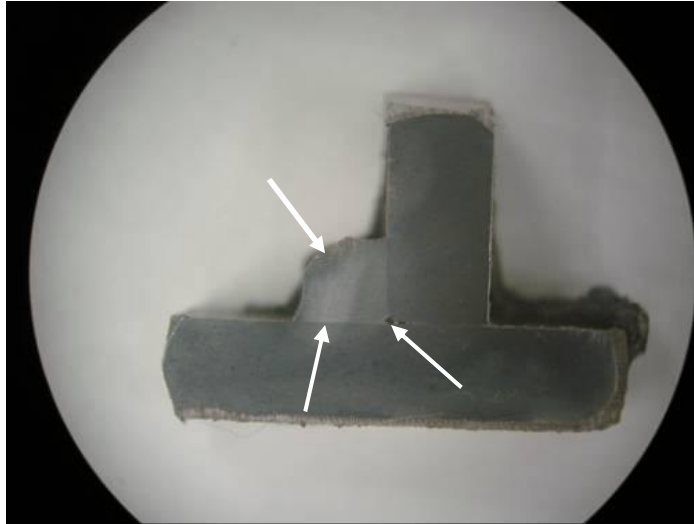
Cordão de solda com pouca fusão na flange e alma CP 97.1.
